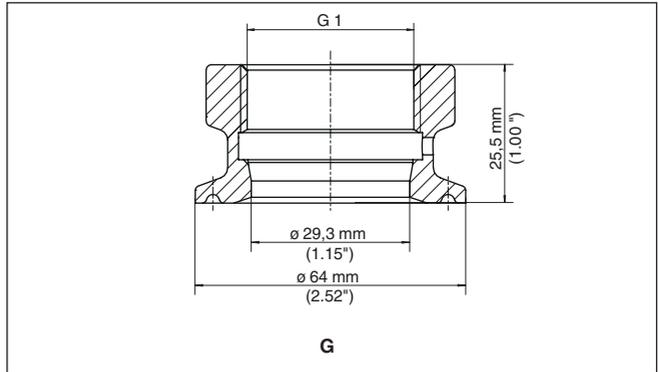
Dimensiones adaptador de rosca G1 (DIN 3852-X) a Clamp 2" (DIN 32676, ISO 2852) PN 16
